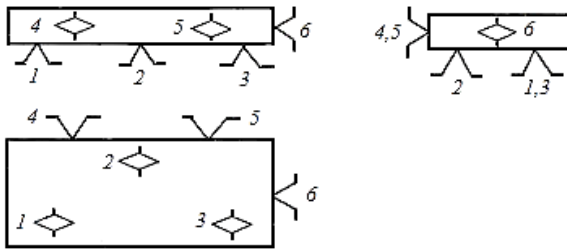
Схема базування призматичної заготовки по плоским поверхням [2]
